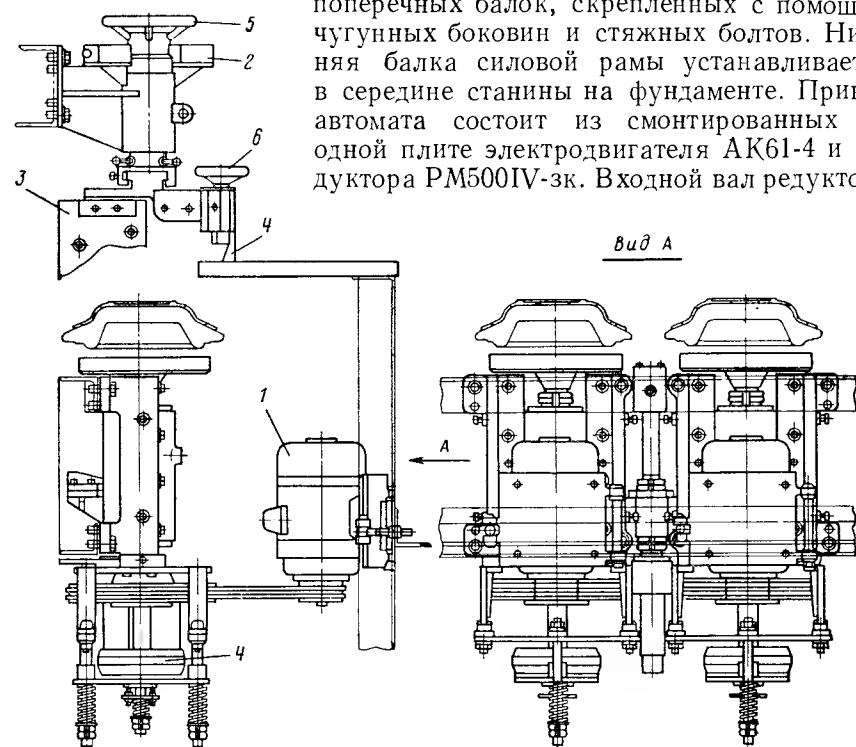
Размещение шпинделя формовочной головки и приводного мотора
